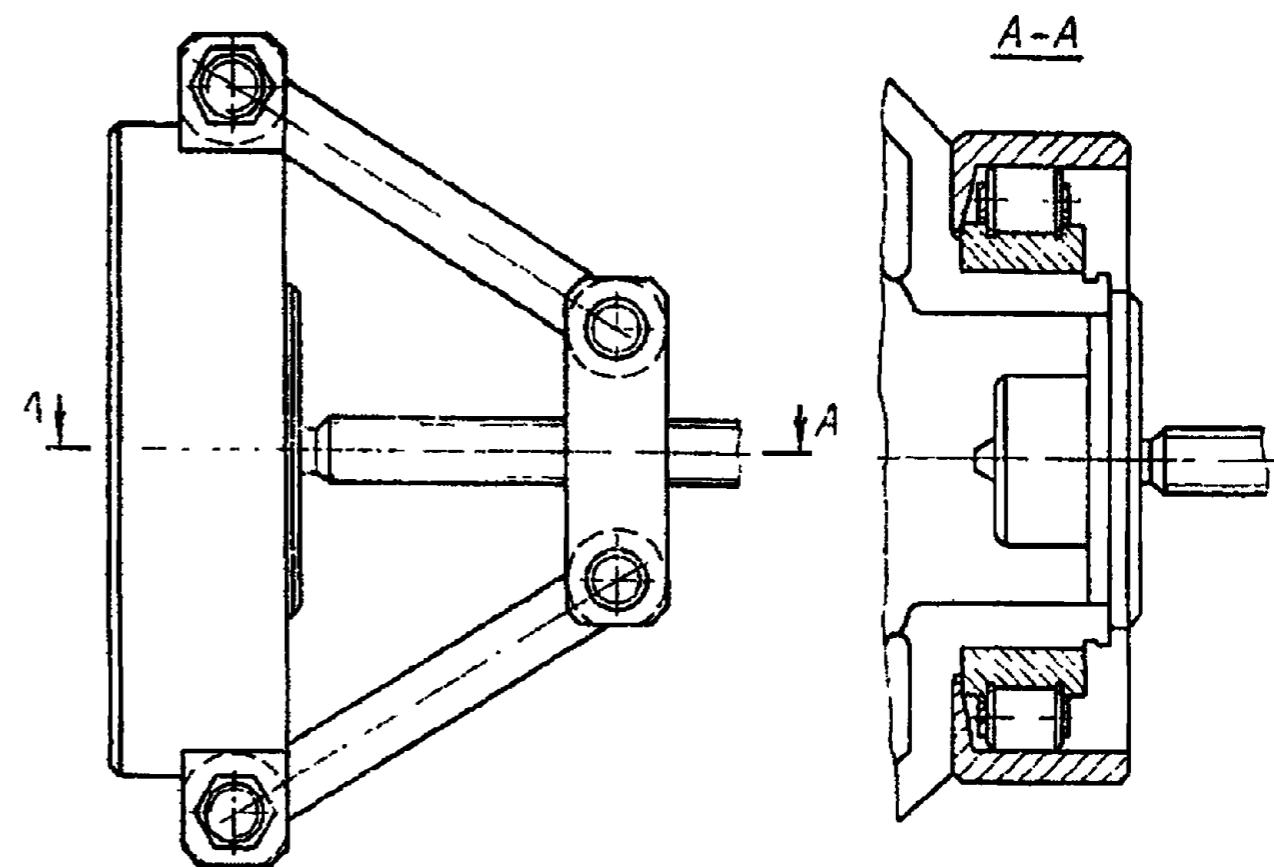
Снятие внутреннего кольца роликоподшипника зубчатого колеса низшей передачи привода заднего моста
